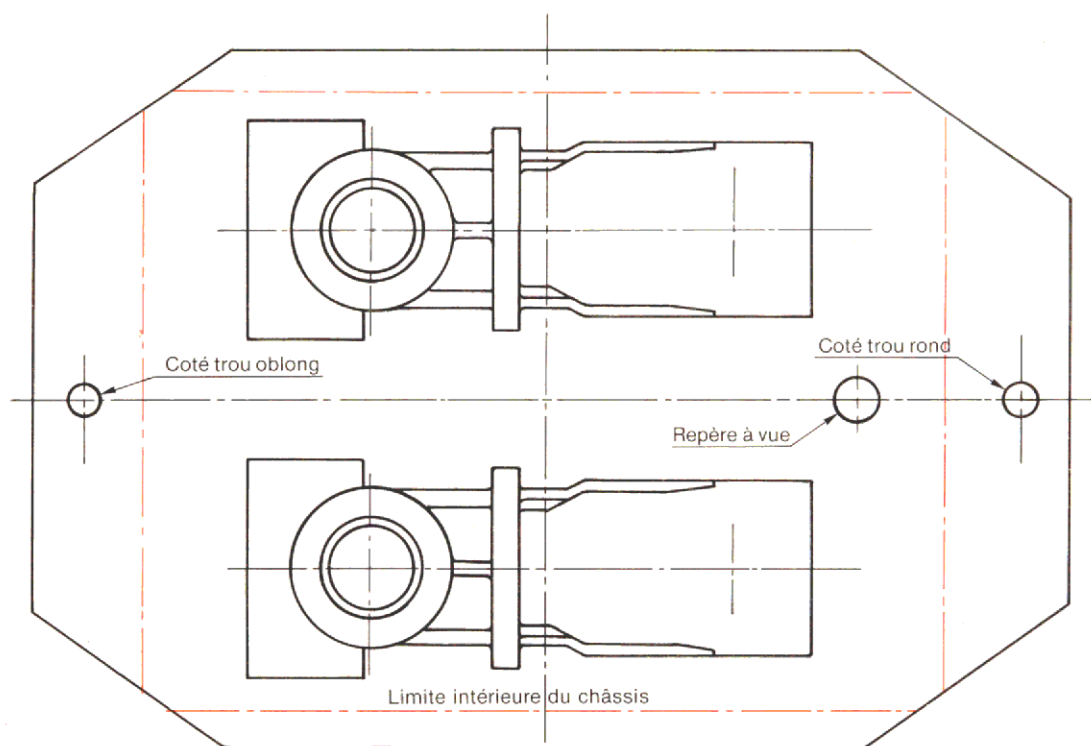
Plaque modèle pour châssis de dessous.
